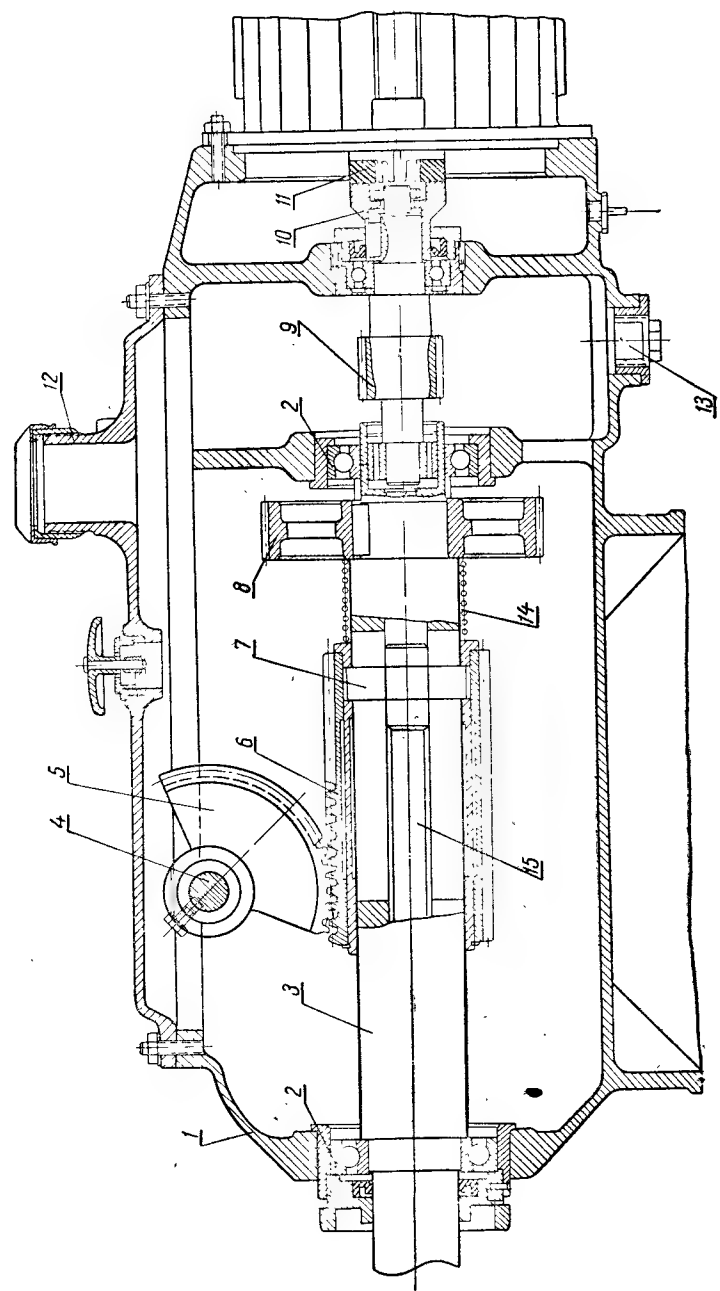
Редуктор ветроэлектрического агрегата ВЭС-1-5:
